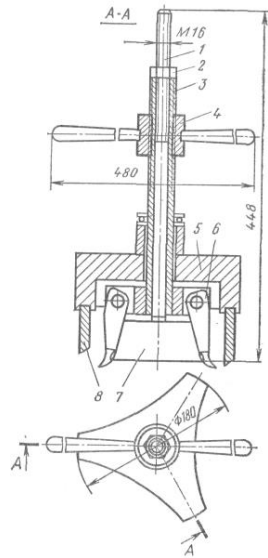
Гвинтовий знімач зовнішнього кільця роликового підшипника стакана підшипників ведучої шестерні кінцевої передачі: 1- гвинт; 2 і 4- гайки, 3- силовий гвинт; 5- корпус; 6- захоплювач; 7- конус; 8- стакан.
